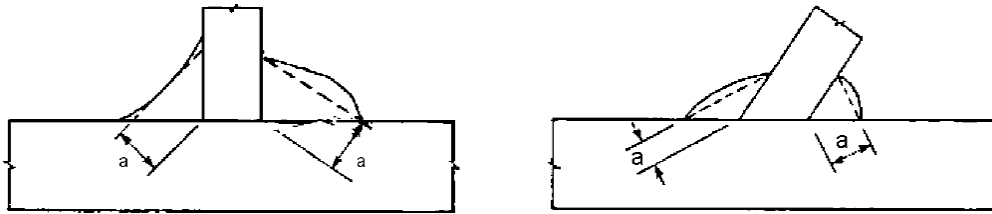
Espesor de garganta de una soldadura en ángulo
